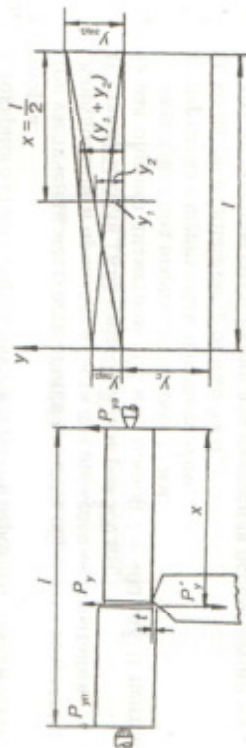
Схема упругих деформаций узлов токарного станка
